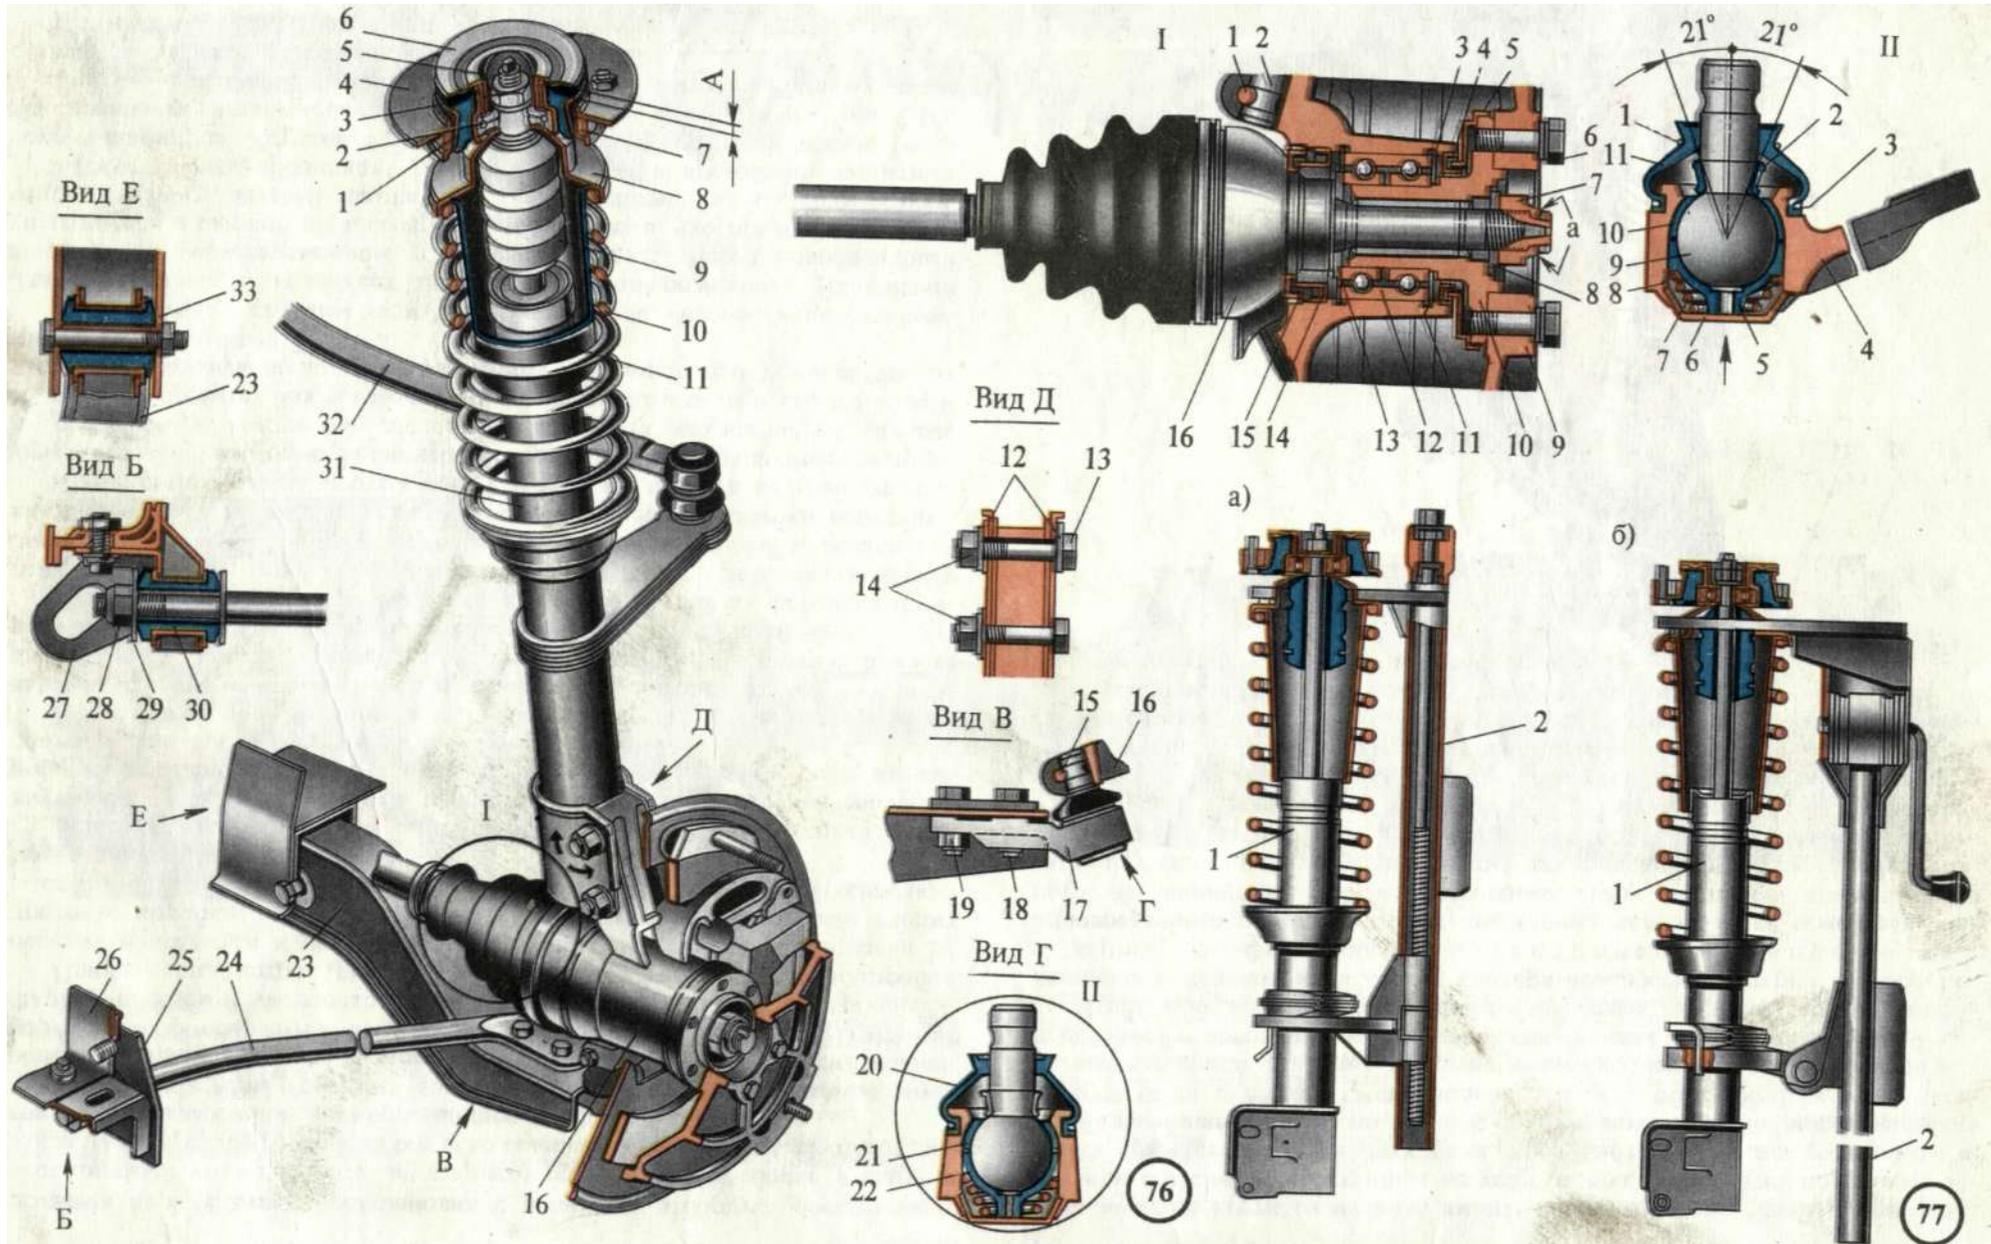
Передняя подвеска в сборе с шарнирным валом (левая сторона):
